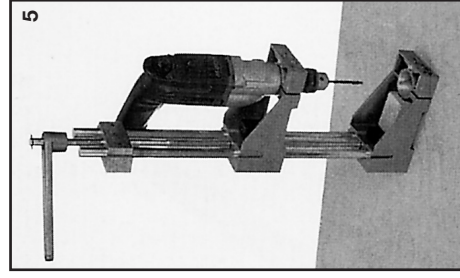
9: Detaillierte Montageanleitung wird mit Bohrplatte geliefert.
